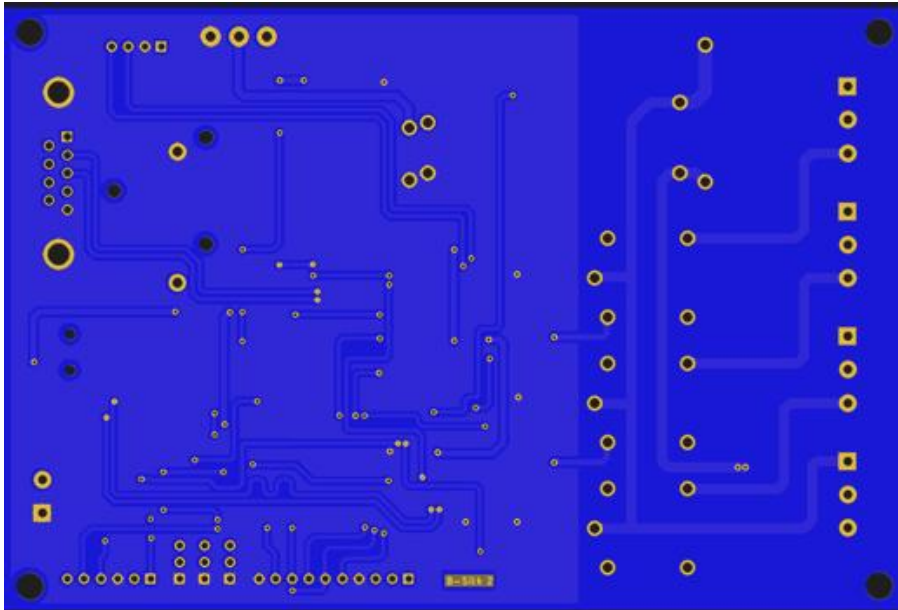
Layout Inferior da Placa de Circuito Impresso.
